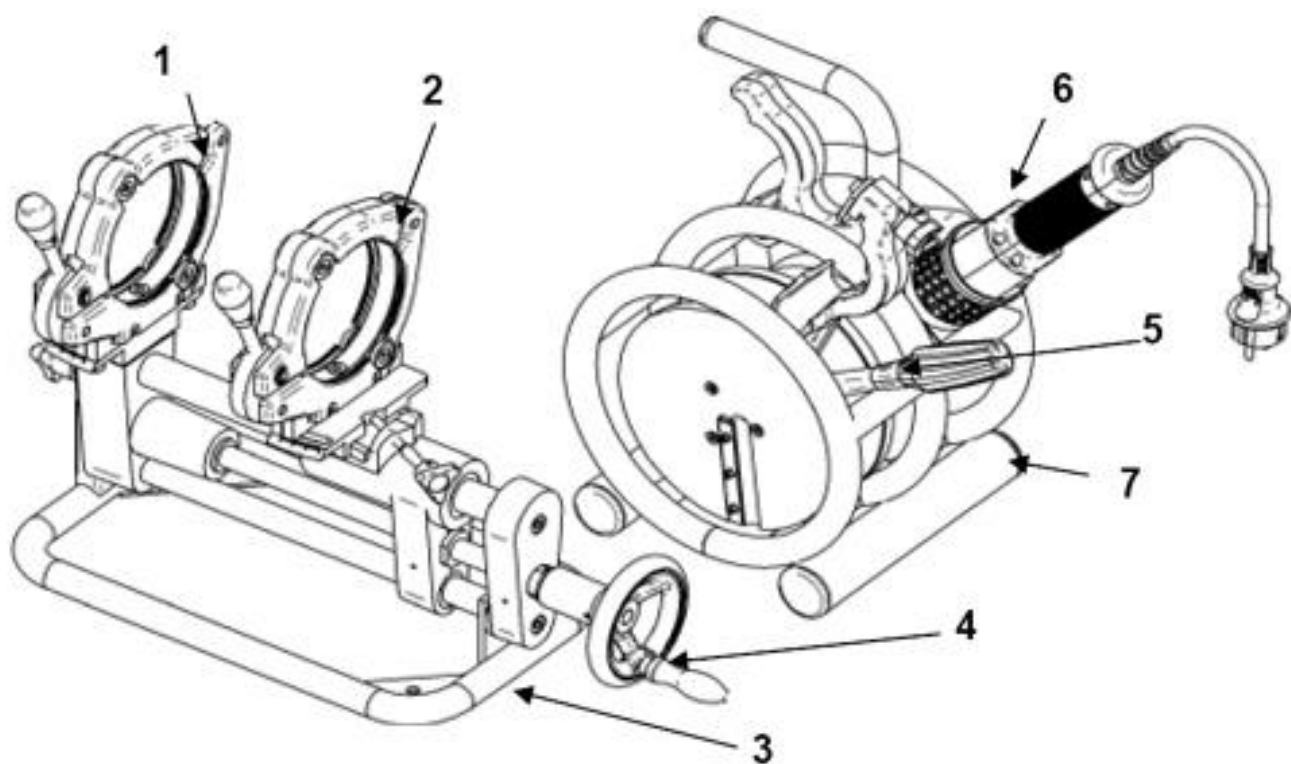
Состав оборудования с механическим приводом для стыковой сварки
